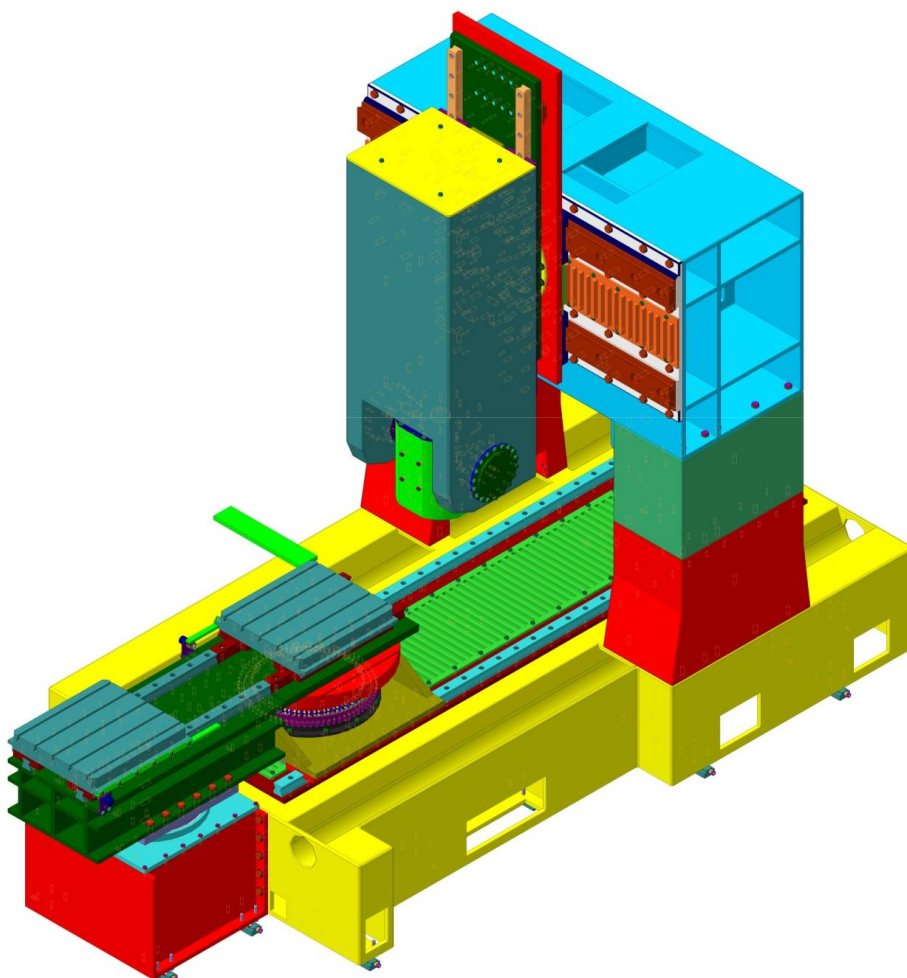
модель сборки пятикоординатного обрабатывающего центра портальной компоновки
